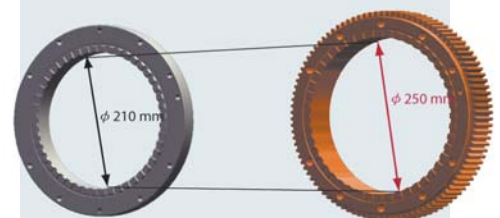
Увеличение диаметра зубчатого колеса торцевой муфты револьвера
